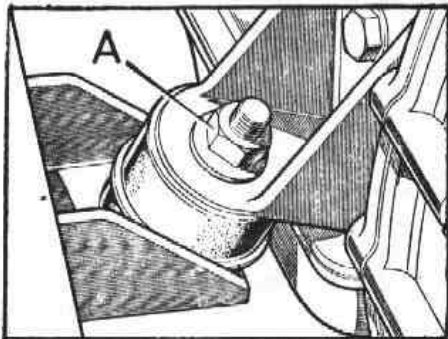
Desmontaje de las tuercas que fijan el motor a sus tacos de apoyo
